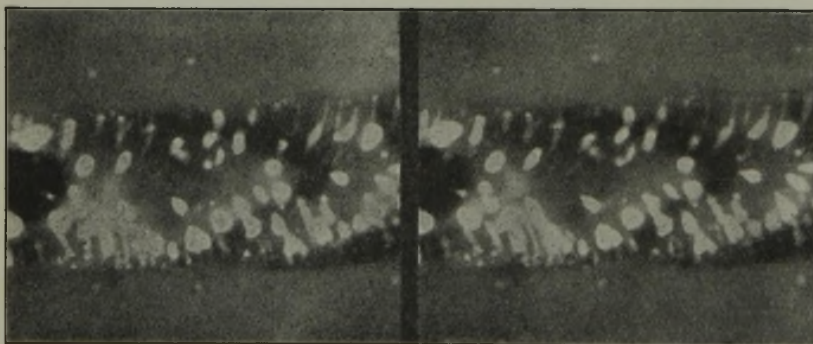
Stereobilder einer Schweißung mit Kohlenlichtbogen.
